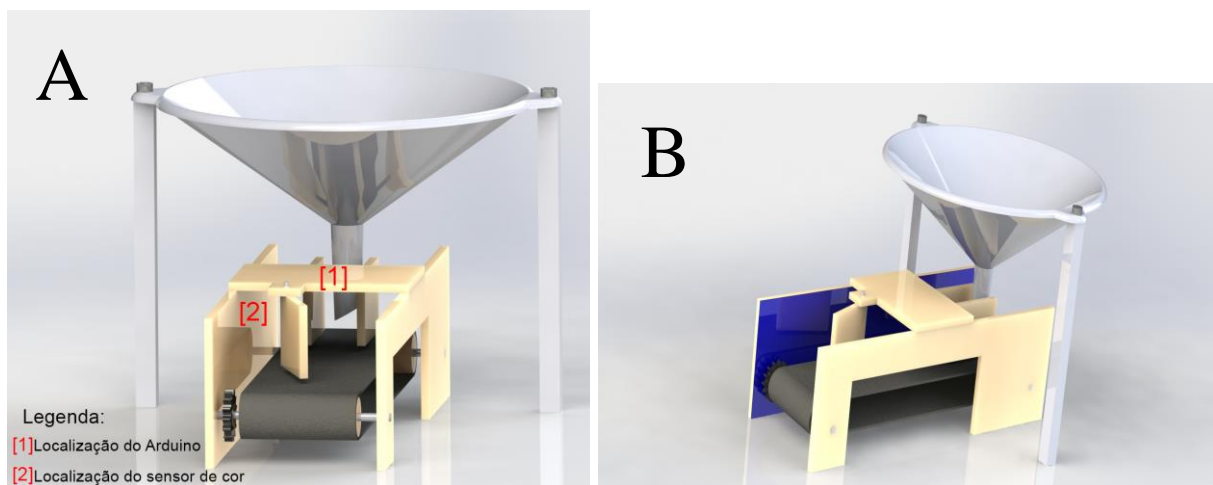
Vista isométrica do modelo desenvolvido na ferramenta de CAD 3D SolidWorks (A); vista com lado em que o sensor será instalado destacado (B).
